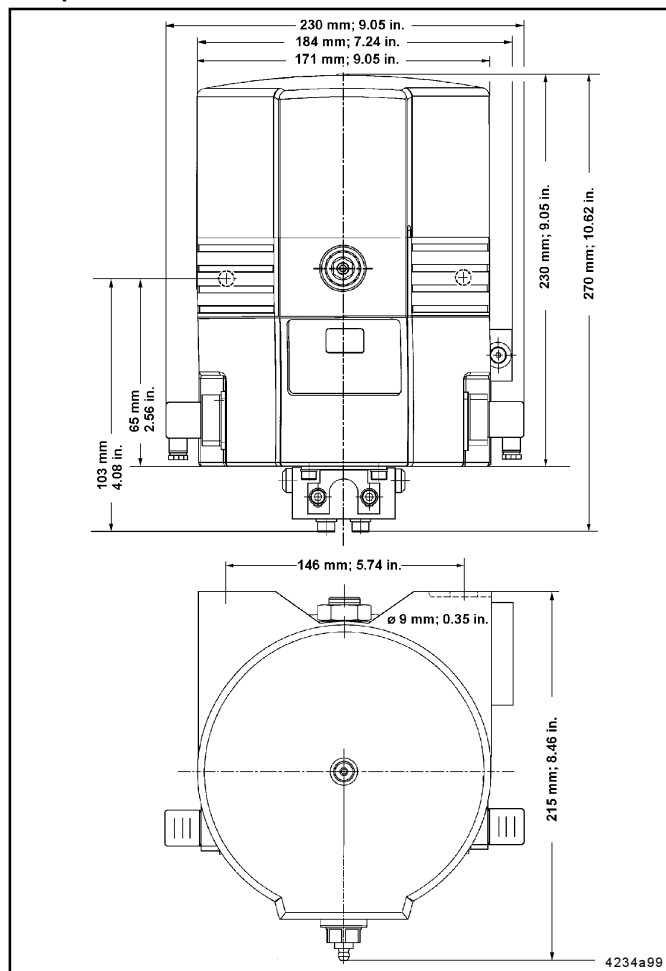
Cotes dimensionnelles de la pompe QLS 301
